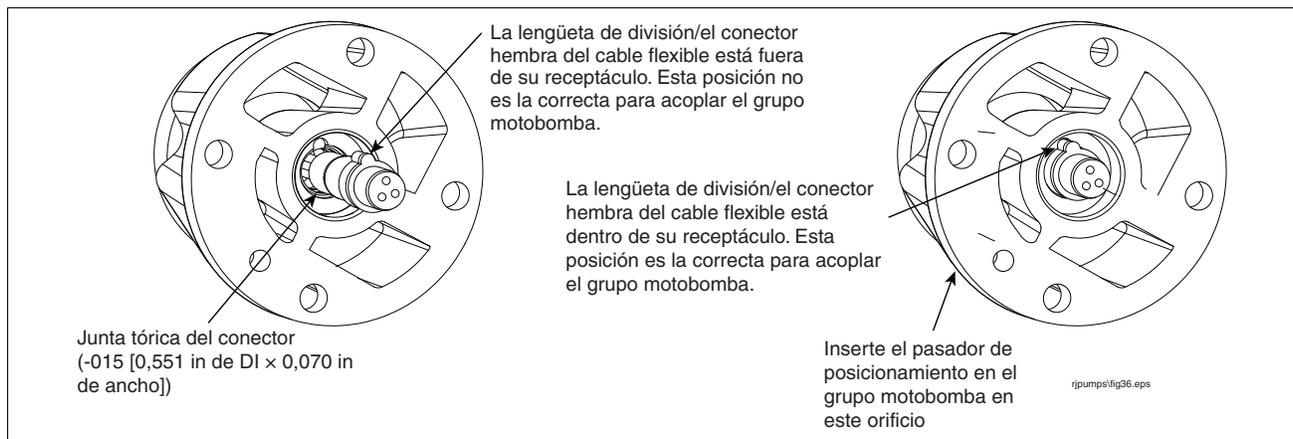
Compruebe que el conector hembra del cable flexible esté bien colocado
